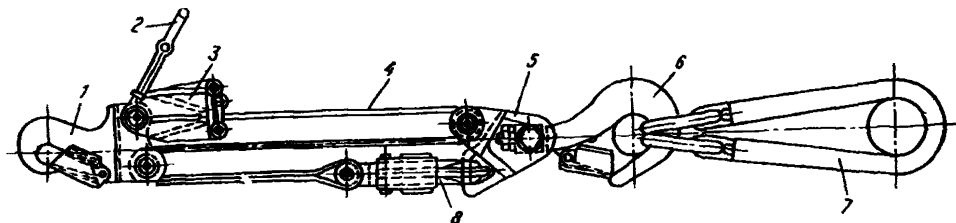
Швартовочный ремень (по самолет № 02010):
